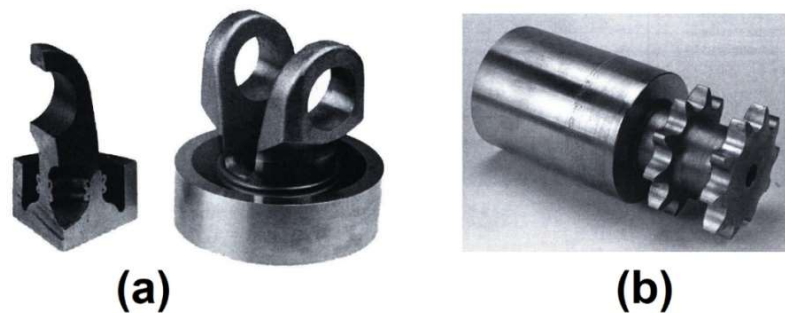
a) Piston d'un moteur diesel. b) Remplacement de pièces forgées ou coulées par des profilés standards [9].
